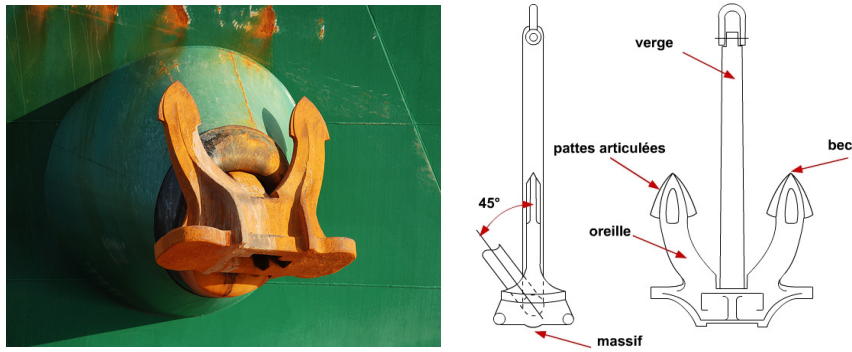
Ancre articulée type Hall (photo Ronan Dolain)
